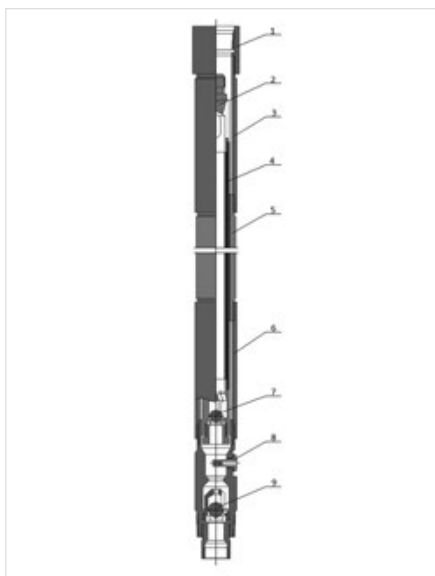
Насос невставной скважинный штанговый с коротким цилиндром типа ННБКУ
